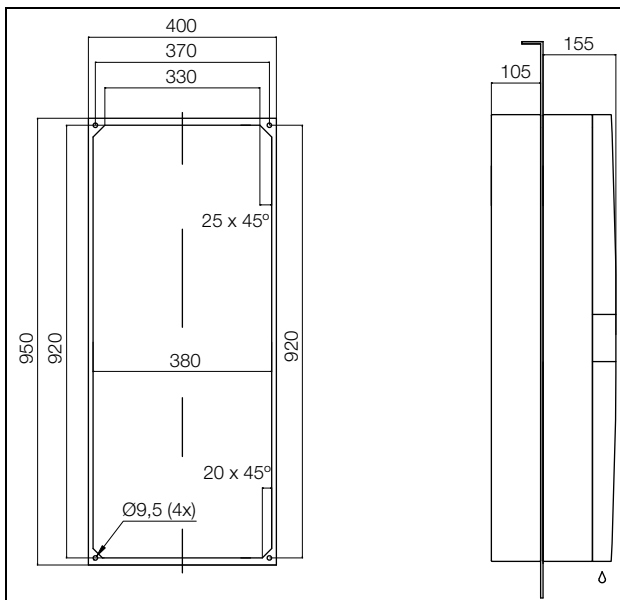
3304.xxx, 3305.xxx полутопленный монтаж
